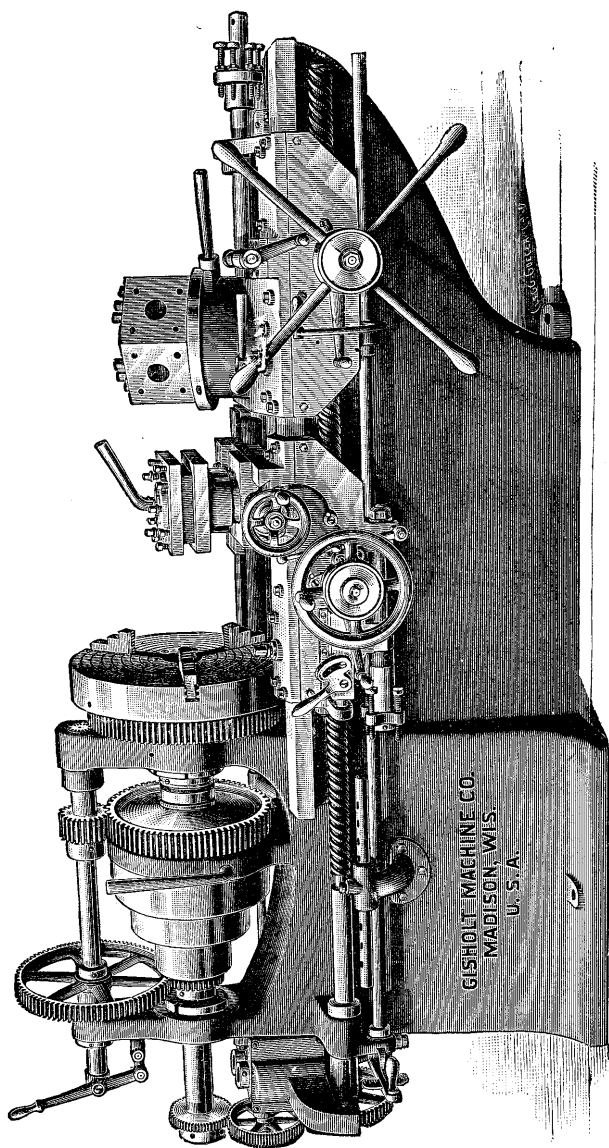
Tour à revolver de la Gisholt Machine Company, de Madison (E.-U.).
